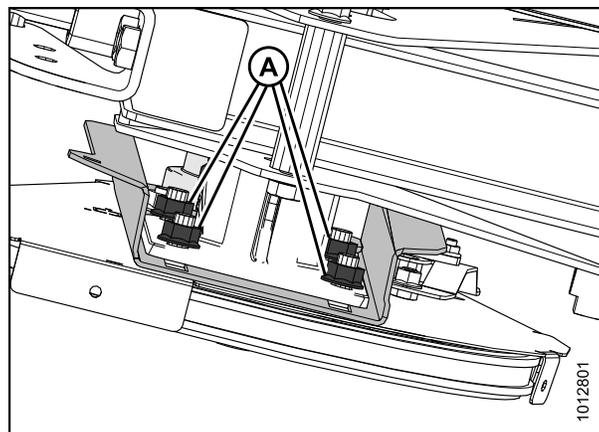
Привод единого мотовила — вид со стороны нижней части мотовила
